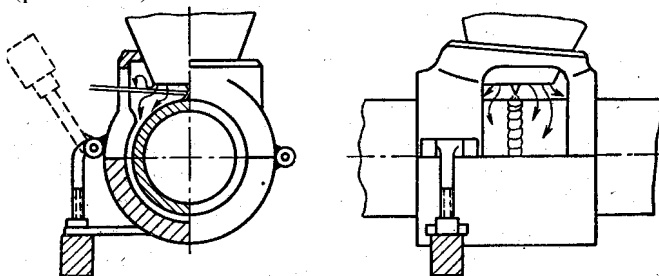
Газозащитная камера для аргоно-дуговой сварки труб
